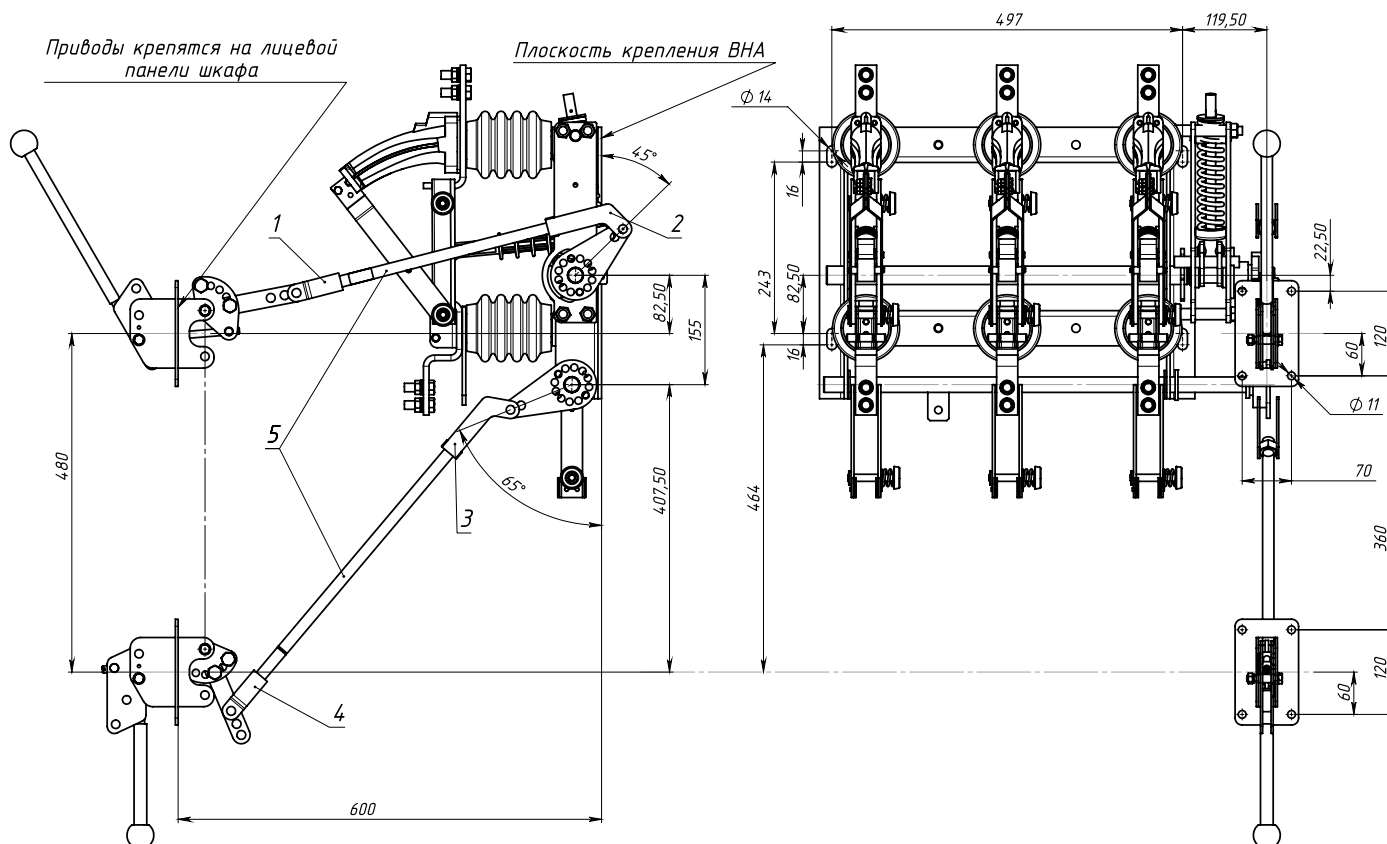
Возможный монтаж выключателя нагрузки с приводом ПР-10-СТ.
